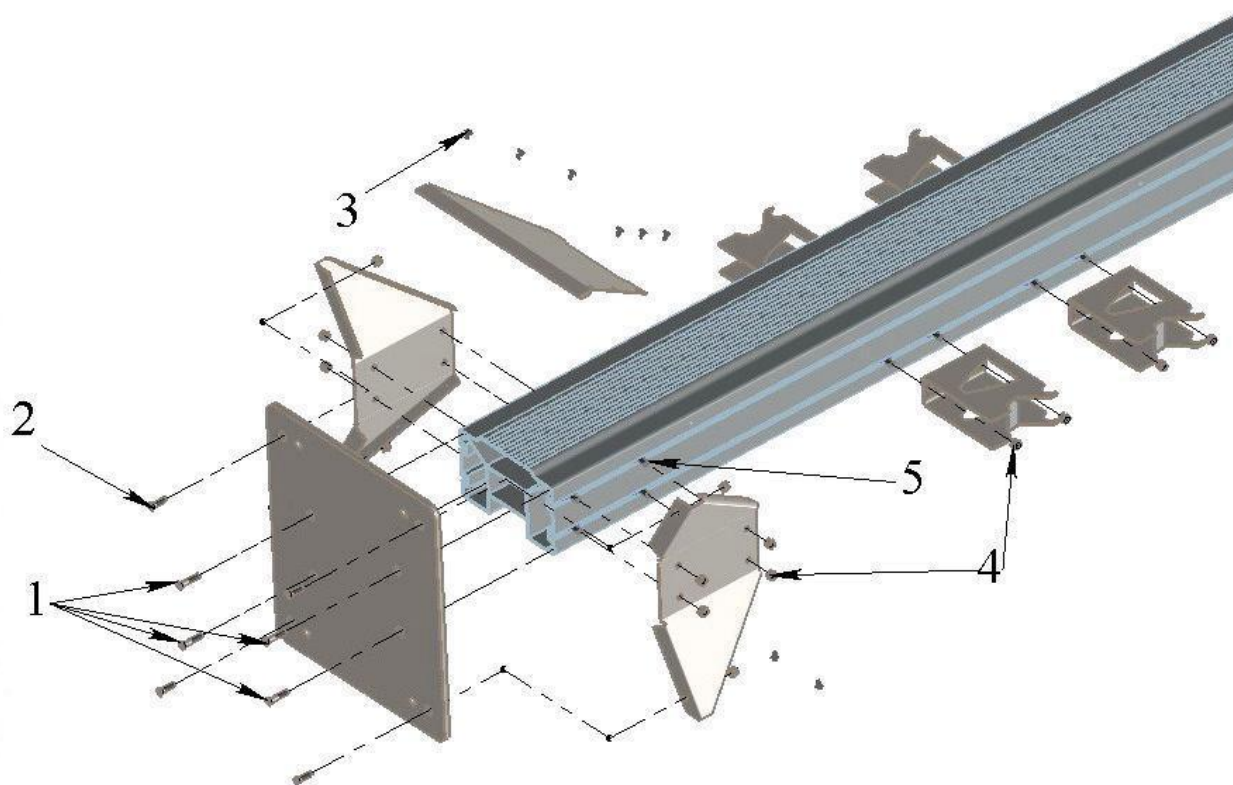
Установка основания. 1 – винт М8х40 (саморез 7,5х52); 2 – винт М8х25; 3- черный саморез с пресшайбой 4,2х16; 4- гайка М8 с шайбой; 5- вставка с болтом М8х20.
